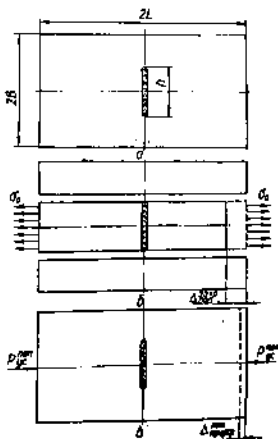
Расчетная схема определения продольного укорочения от сварки поперечного шва
